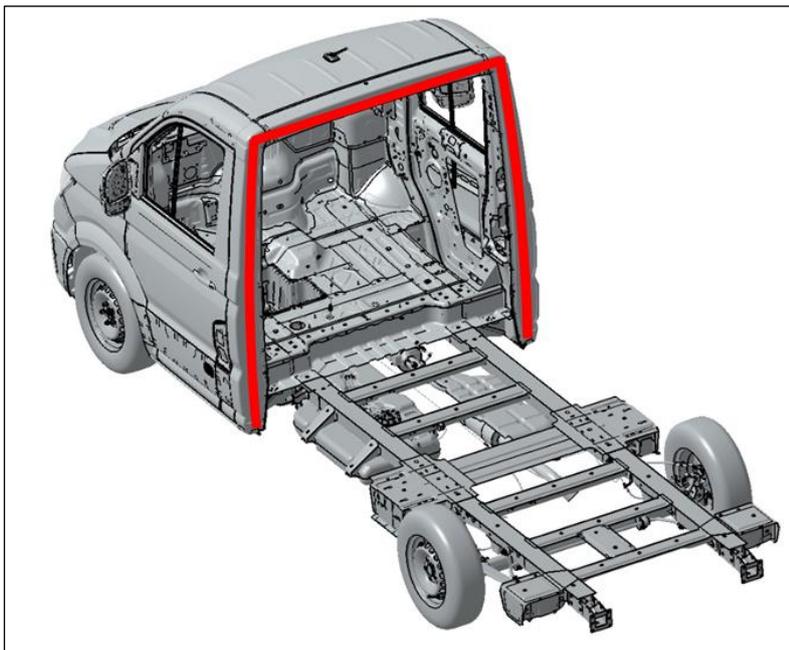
Crafter avec châssis à cadre plat – Surfaces de collage pour l'assemblage de la cloison arrière de caisse avec traverse de pavillon et montant B de la cabine (schéma de principe de la surface du cadre)
